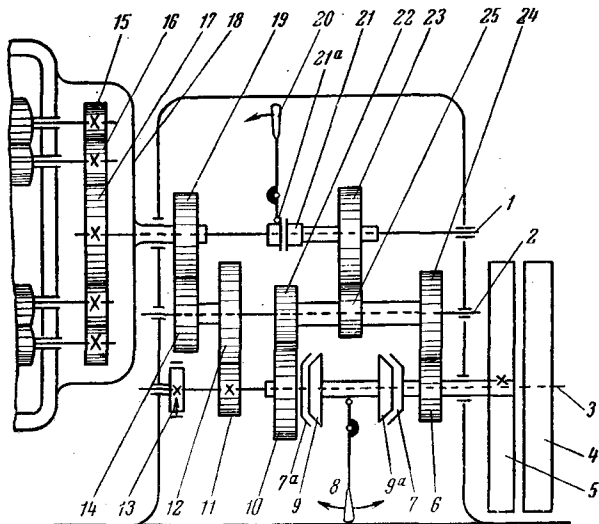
Схема приводного механизма маслоизготовителя с двумя парами вальцов:
